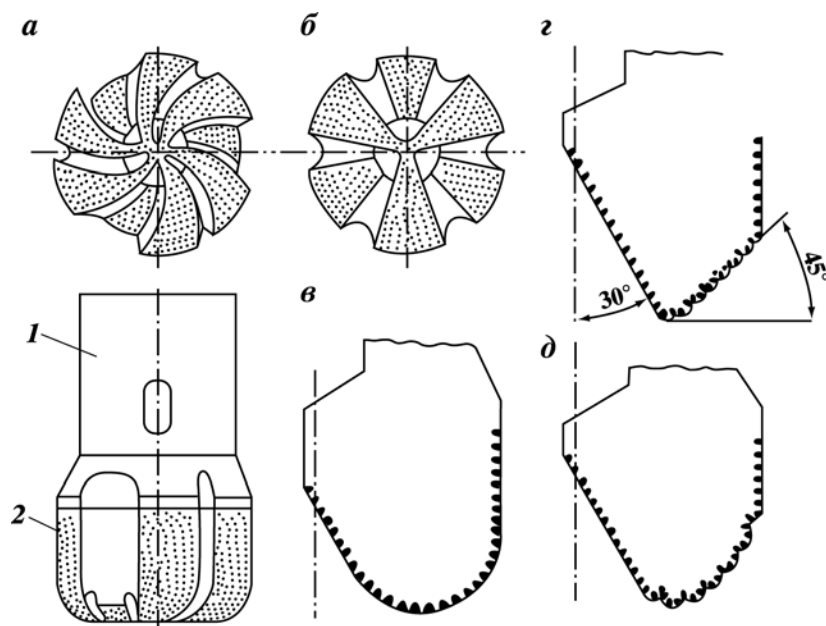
Схемы конструкций алмазных (классических) долот различных типов (а, б) и профили рабочих поверхностей (в, г, д):
